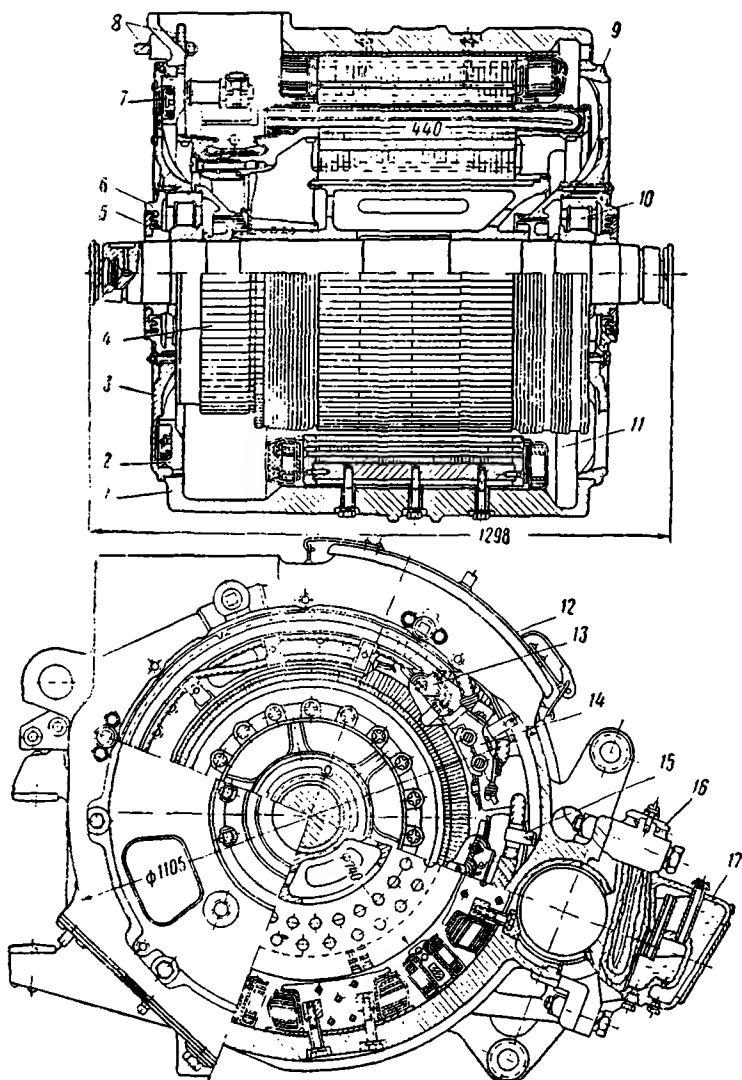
Продольный и поперечный разрезы двигателя типа НБ-412М:
